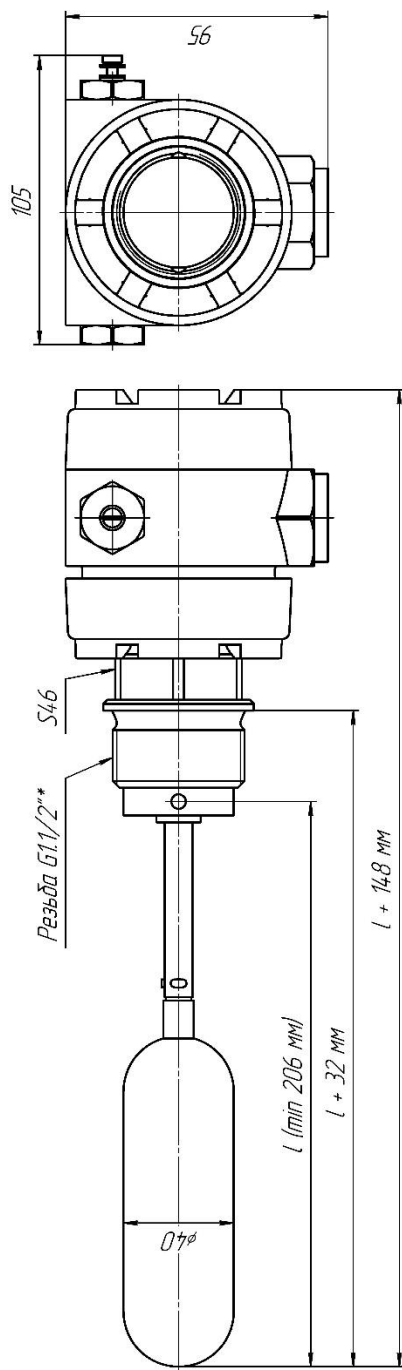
Общий вид сигнализатора уровня с присоединительной резьбой G1.1/2"
